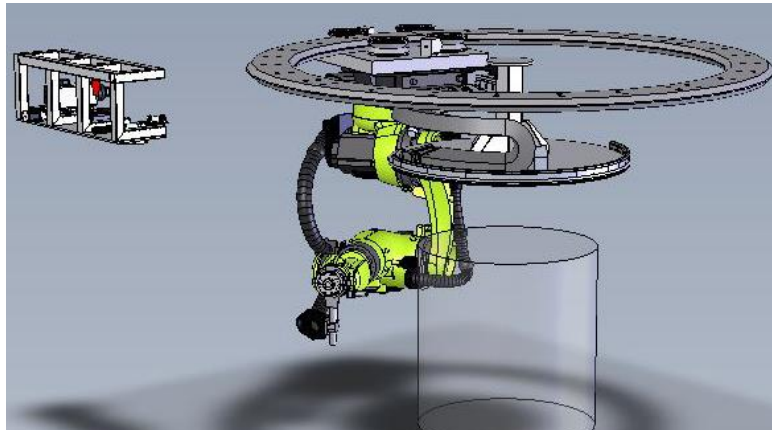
Diseño de un sistema automatizado de inspección y reparación por soldadura en celda caliente
